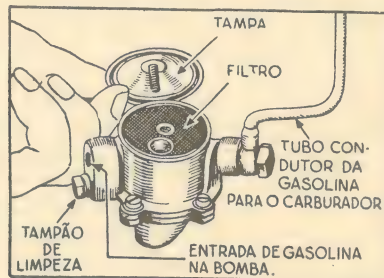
Bomba de gasolina com a tampa levantada, mostrando o filtro
